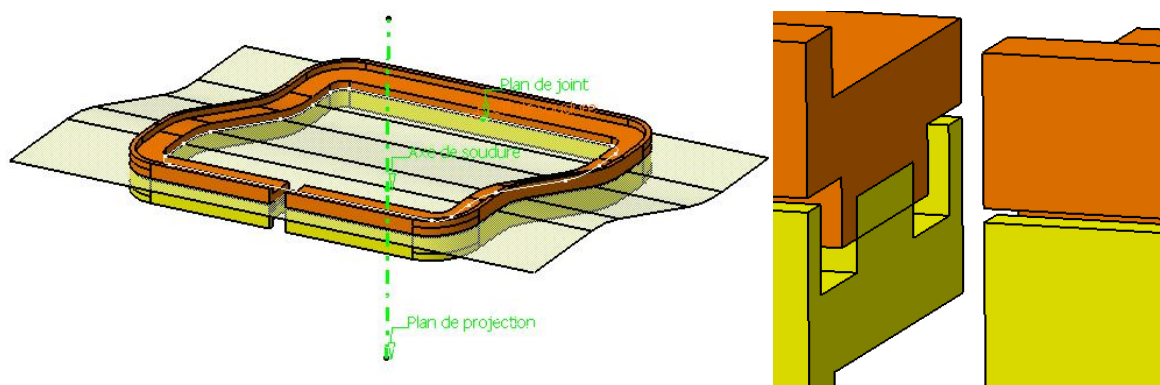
Modèle CAO avancé du cordon de soudure par vibration.
